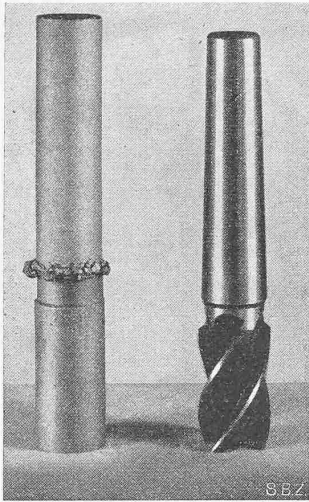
Stumpfgeschweisster Fingerfräser, links roh, rechts fertig bearbeitet
